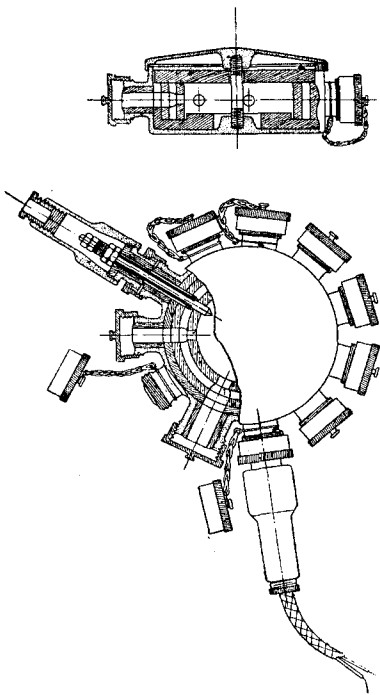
Caja metálica de empalme de 11 direcciones. Vista y corte vertical; planta y corte horizontal.
